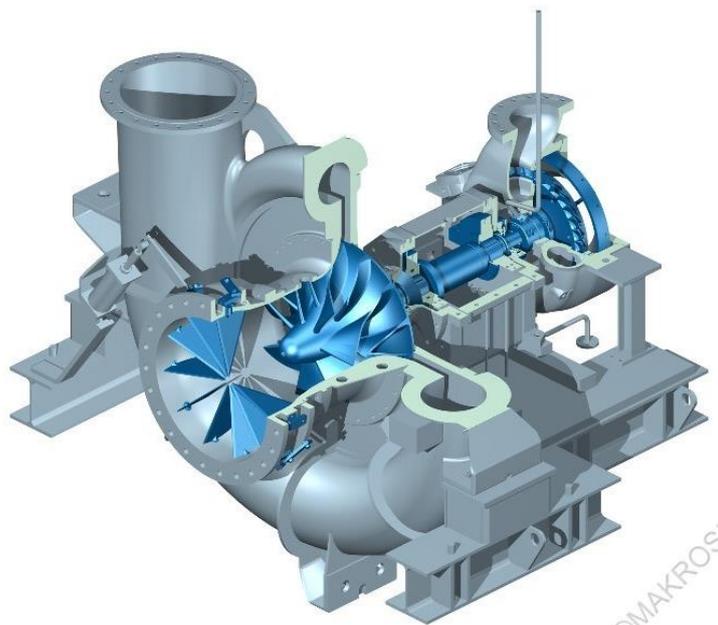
Современный турбодетандерный агрегат в разрезе [2]
